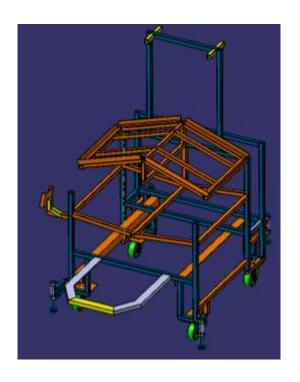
3D модель телеги R для транспортировки деталей
